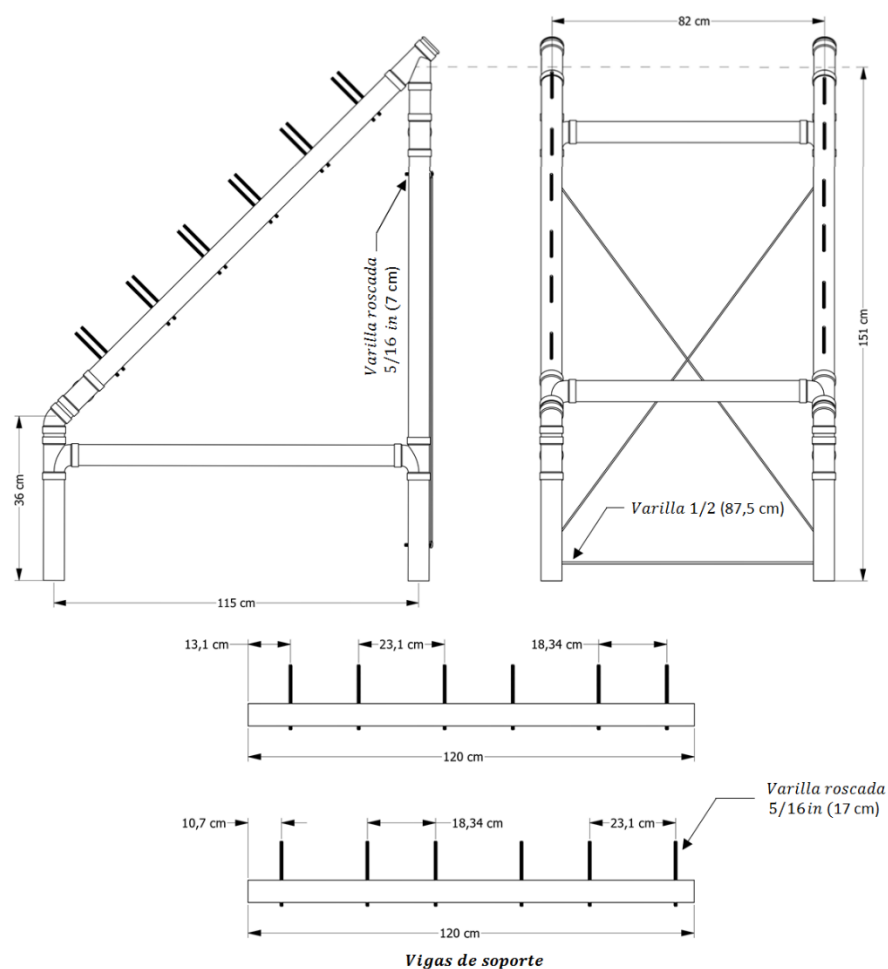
Planos del sistema NFT con las vigas de soporte (diagonales). Fuente: (Rosero, 2019)
